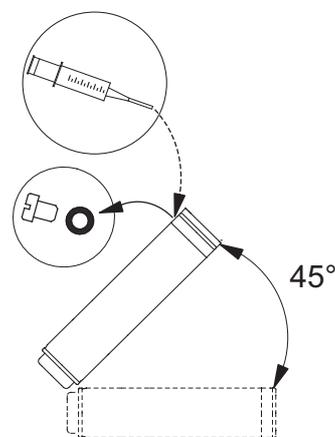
Position des Motors während des Befüllens, MS6 und MS 6000
